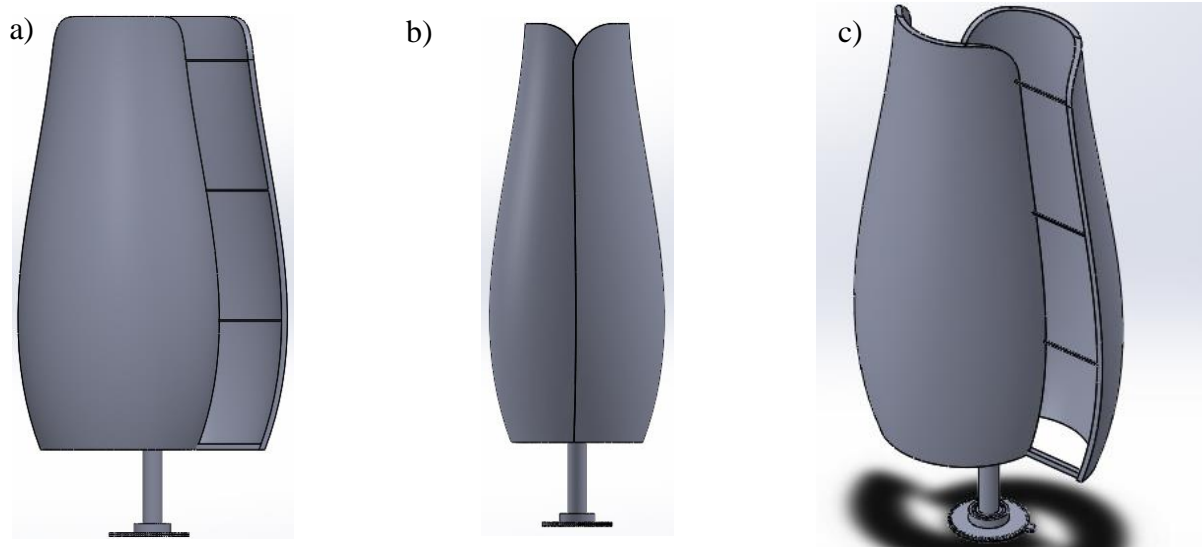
Dibujo de la turbina eólica de Tulipán: a) vista frontal, b) vista lateral, c) vista isométrica. Diseñada con SolidWorks®.
